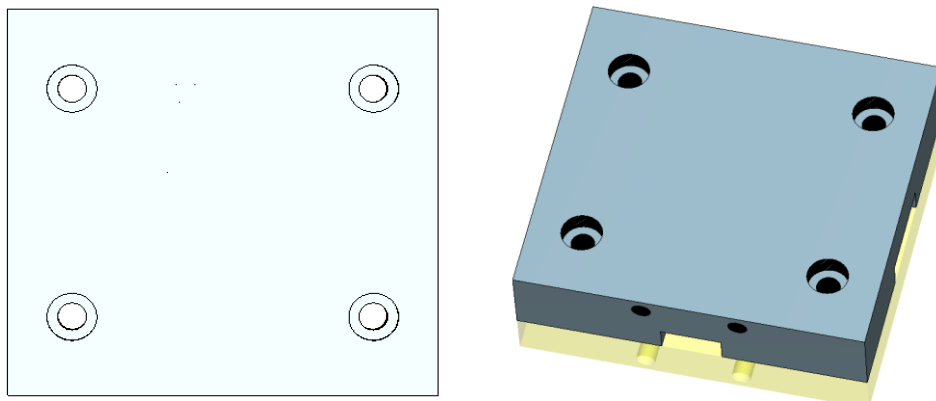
Planta inferior y vista oblicua de la tapa inferior del prototipo.
